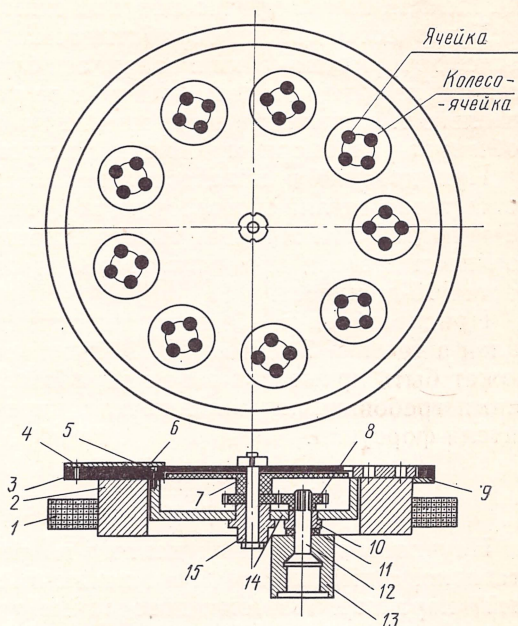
Приспособление с электромагнитной муфтой для удержания деталей
